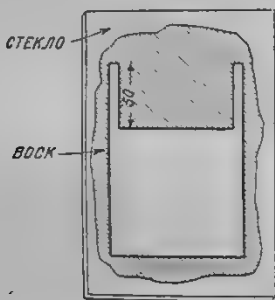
Заготовка формы для отливки аккумуляторной пластины.
